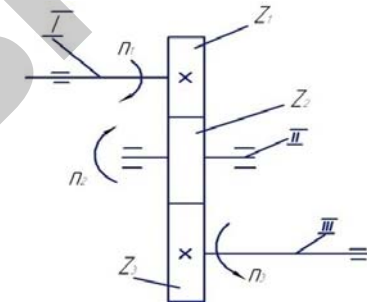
Зубчатая цилиндрическая передача с паразитным колесом
